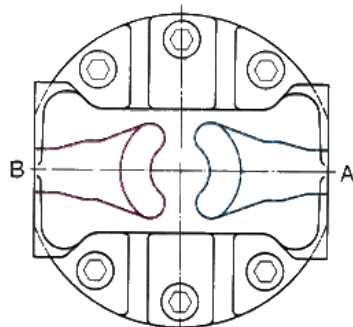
Bomba de pistones axiales con placa inclinada.
